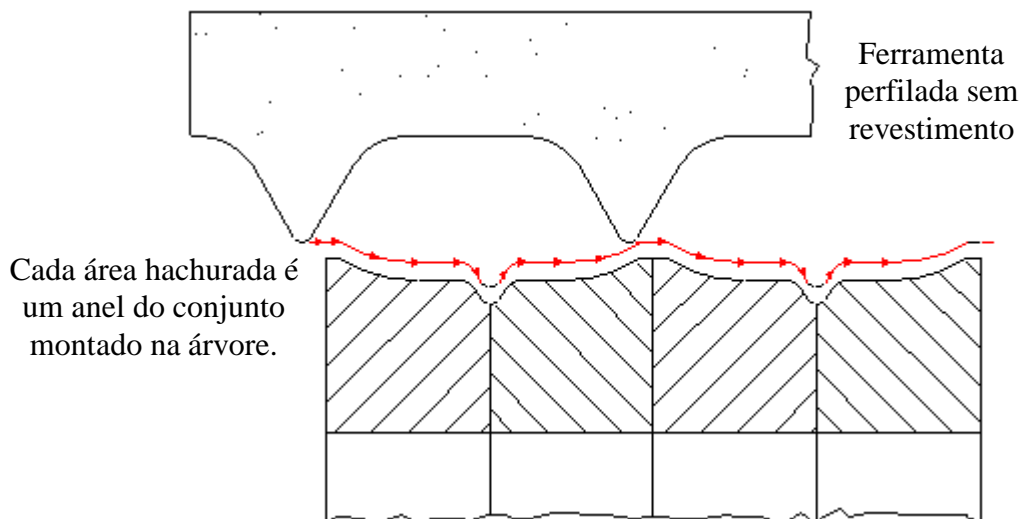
Movimento que a ferramenta perfilada executa durante o torneamento. Fonte: Mahle (2008).
